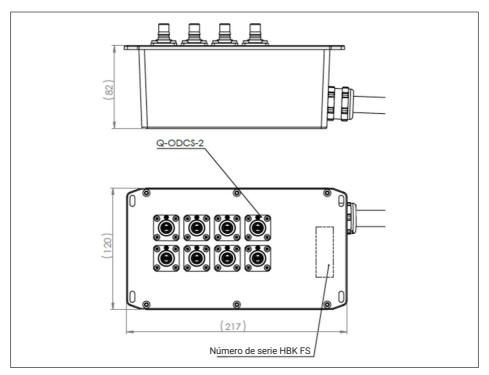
Dibujo técnico de la caja de interconexión – lado de la caja (dimensiones en mm)
